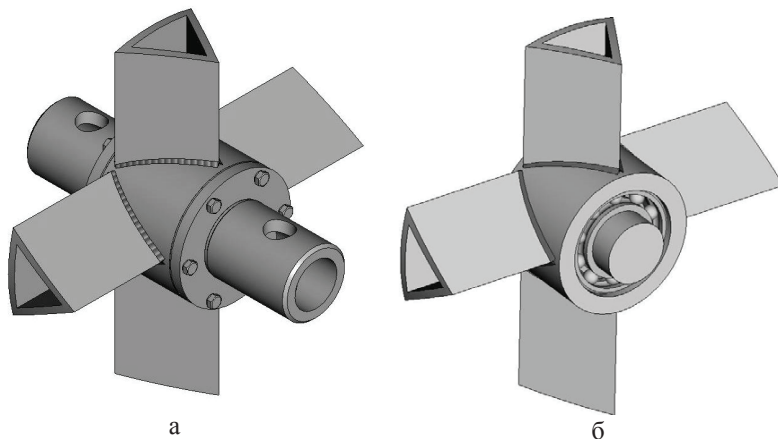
Конструкции опорных подшипниковых узлов с типовыми уплотняющими крышками (а) и без них (б)
